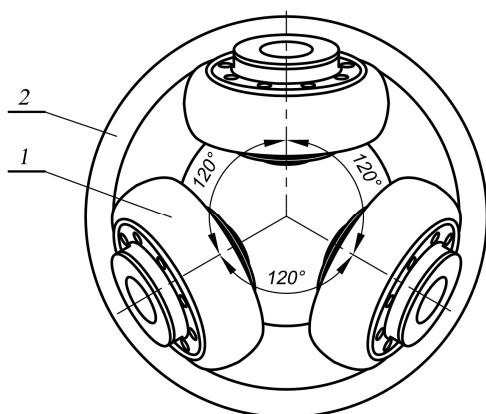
Конструктивная схема расположения мельничных валков на тарели (вид в плане): 1 — размольный валок; 2 — размольная плита (стол)
